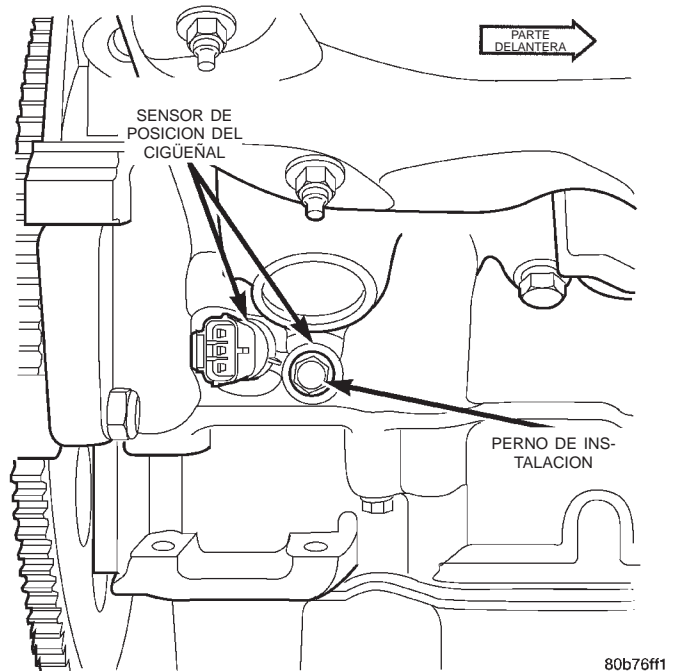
Desmontaje e instalación del sensor de CKP—motor 4.7L V-8
